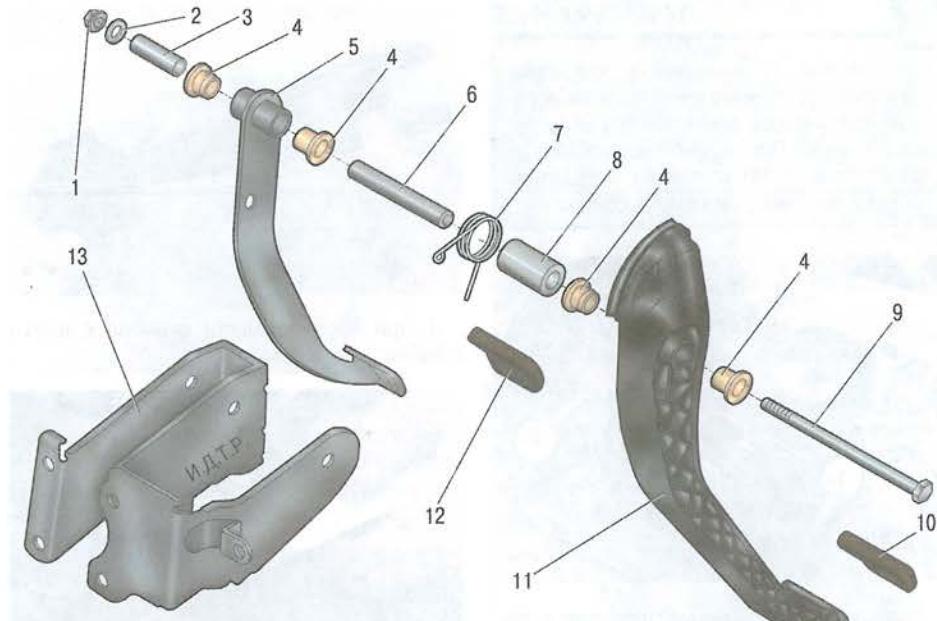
Педальный узел: 1 – гайка оси; 2 – шайба; 3, 6, 8 – дистанционные втулки; 4 – втулка педали; 5 – педаль тормоза; 7 – возвратная пружина педали сцепления; 9 – ось педалей; 10 – накладка площадки педали сцепления; 11 – педаль сцепления; 12 – накладка площадки педали тормоза; 13 – кронштейн педального узла
